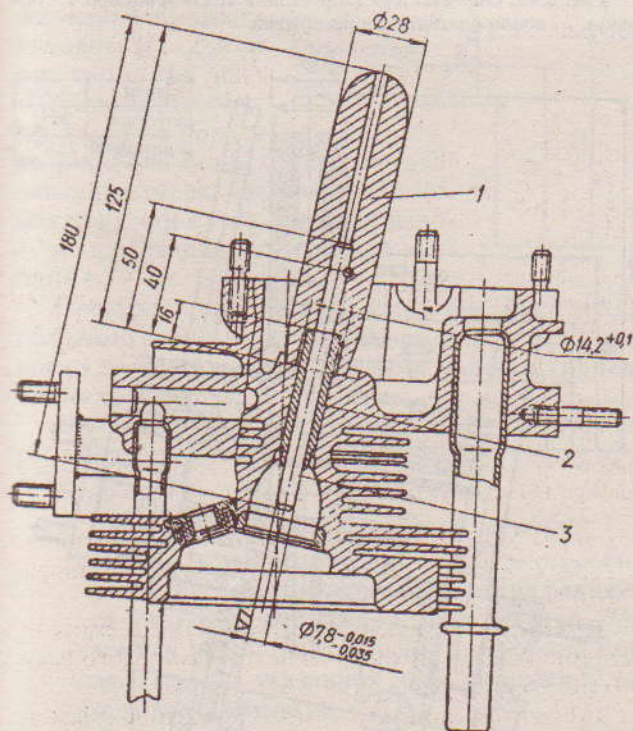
Оправка для запрессовки направляющих втулок клапанов: 1 - оправка; 2 - направляющая втулка клапана; 3 - штифт направляющий
